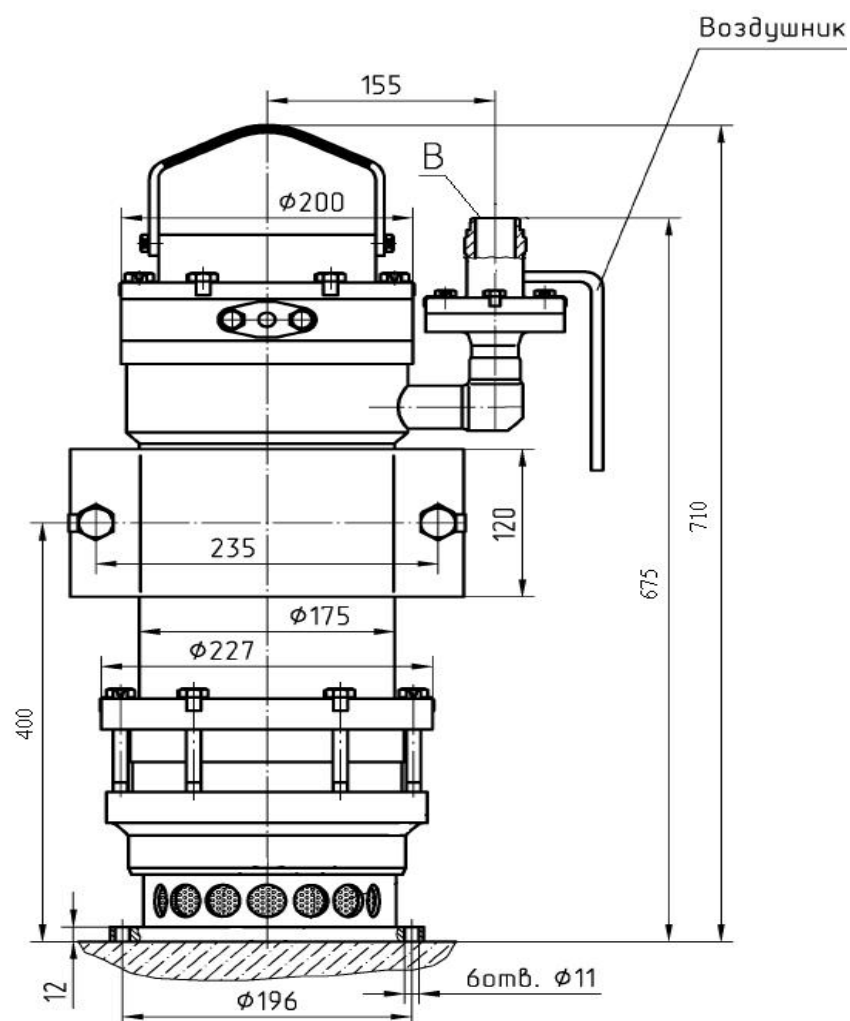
Габаритный чертеж насоса бака боросодержащих дренажей
